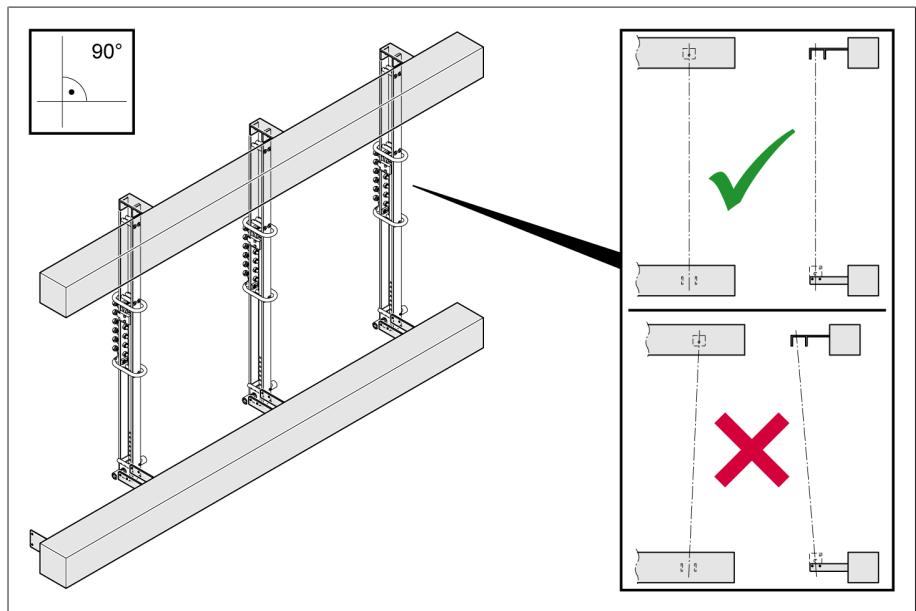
Крепежные приспособления, устройство ПБВ с фронтальным расположением контактов
